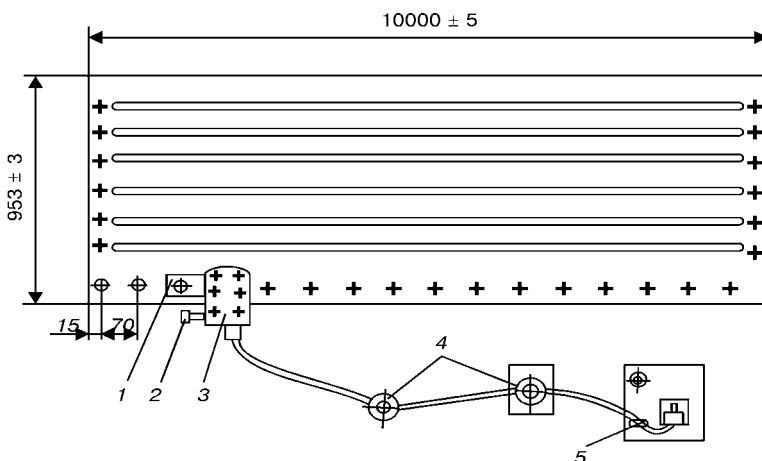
Схема расположения головки-пресса при пробивке отверстий: 1 — установ; 2 — рукоятка; 3 — головка-пресс; 4 — консоль шарнирного типа; 5 — гидрораспределитель
